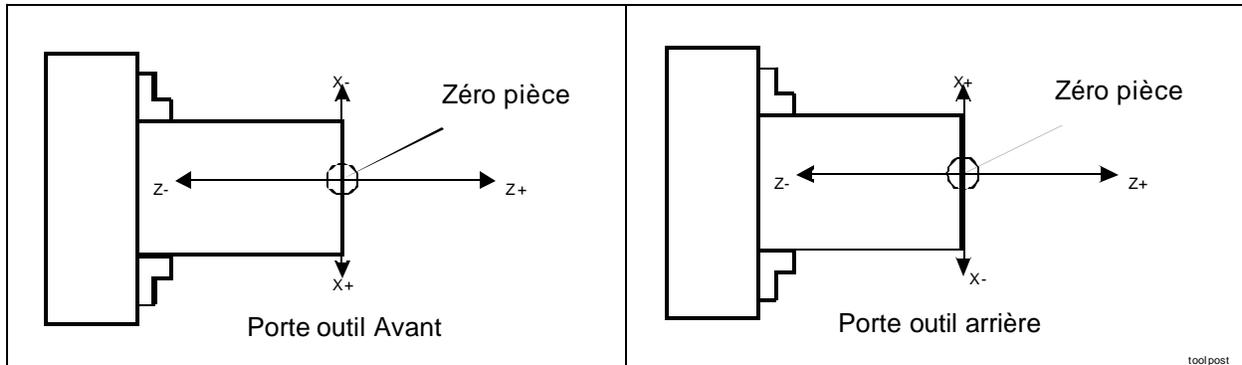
, Sens de déplacement avant / arrière du porte-outils sur l'axe X
